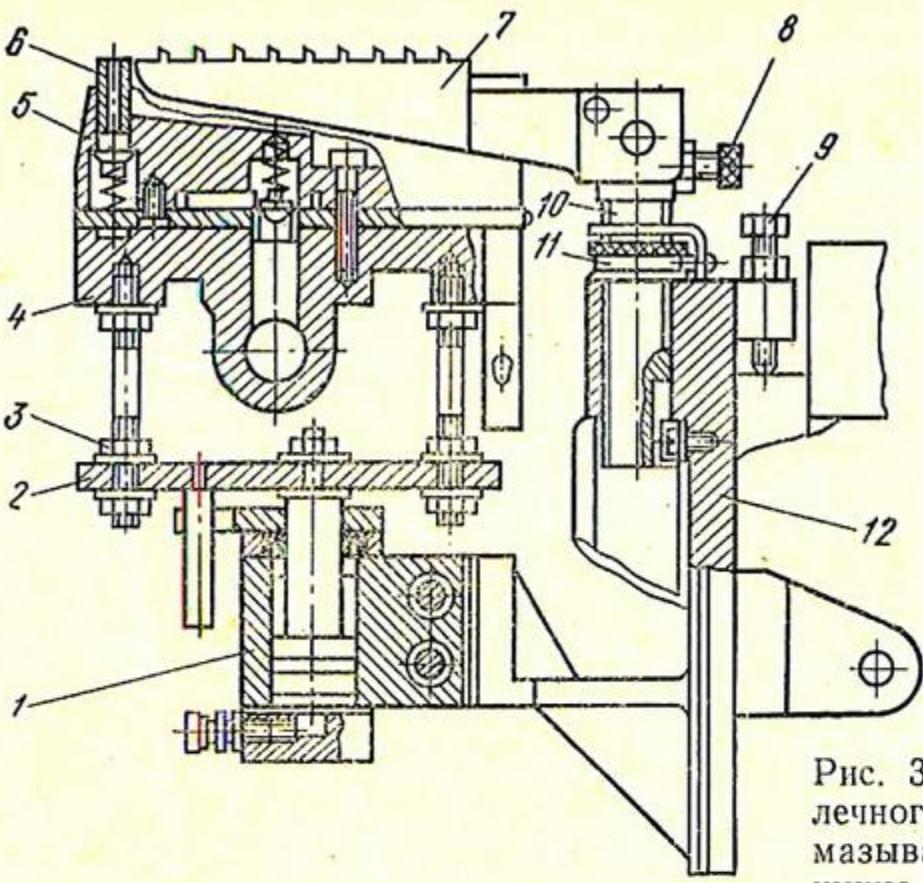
Механизмы стелечного упора и kleенамазывающей обоймы машины ZNK-2M-O
